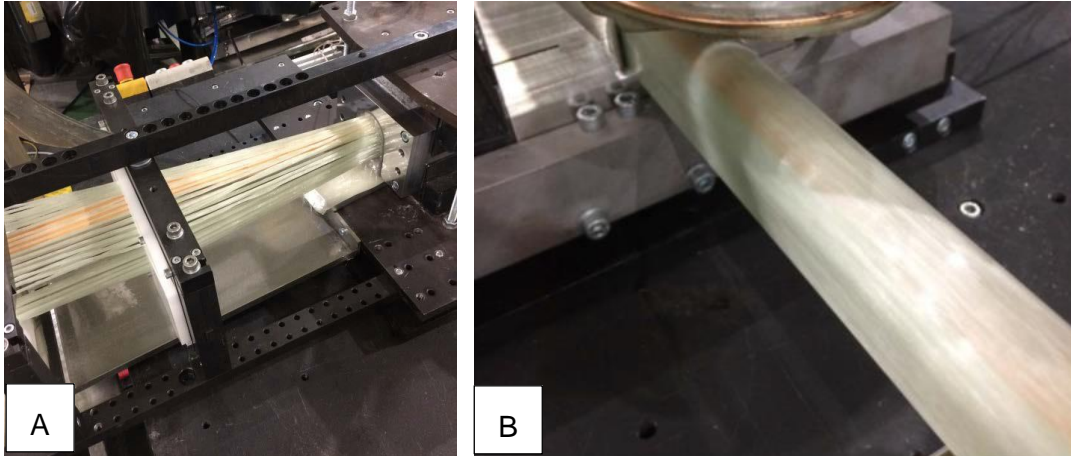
A: Einführung der mit UP-Harz getränkten Glasfasern und des getränkten Furnierbands in das Pultrusionswerkzeug. B: Pultrudiertes Hohlprofil am Werkzeugauslauf (Fotos: David Löpitz, Fraunhofer IWU)
